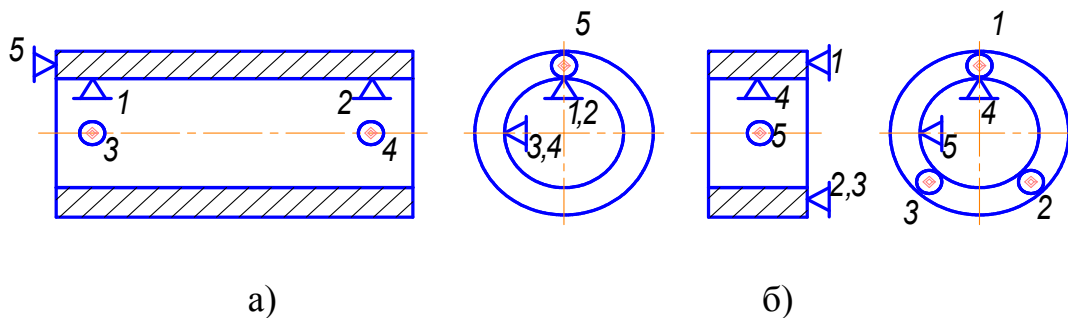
Типовые схемы базирования заготовок по отверстию и торцу
